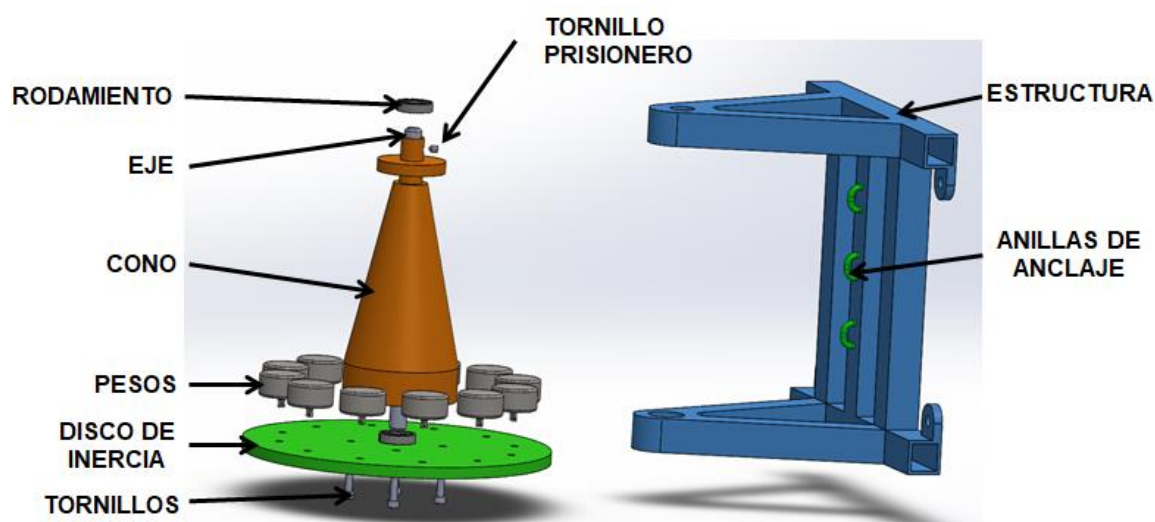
Vista explosión de los componentes del ensamblaje de la polea inercial cónica.
